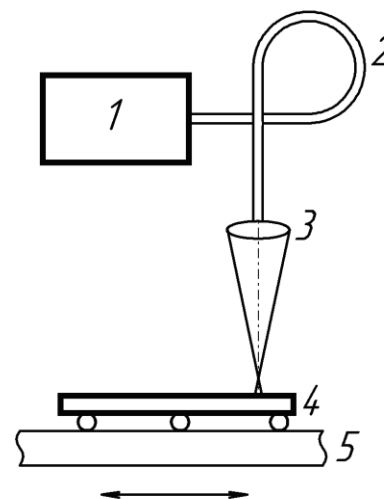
Схема передачи лазерного излучения в зону обработки: 1 – излучатель; 2 – оптоволоконный кабель; 3 – фокусирующая система; 4 – обрабатываемая заготовка; 5 – рабочий стол
